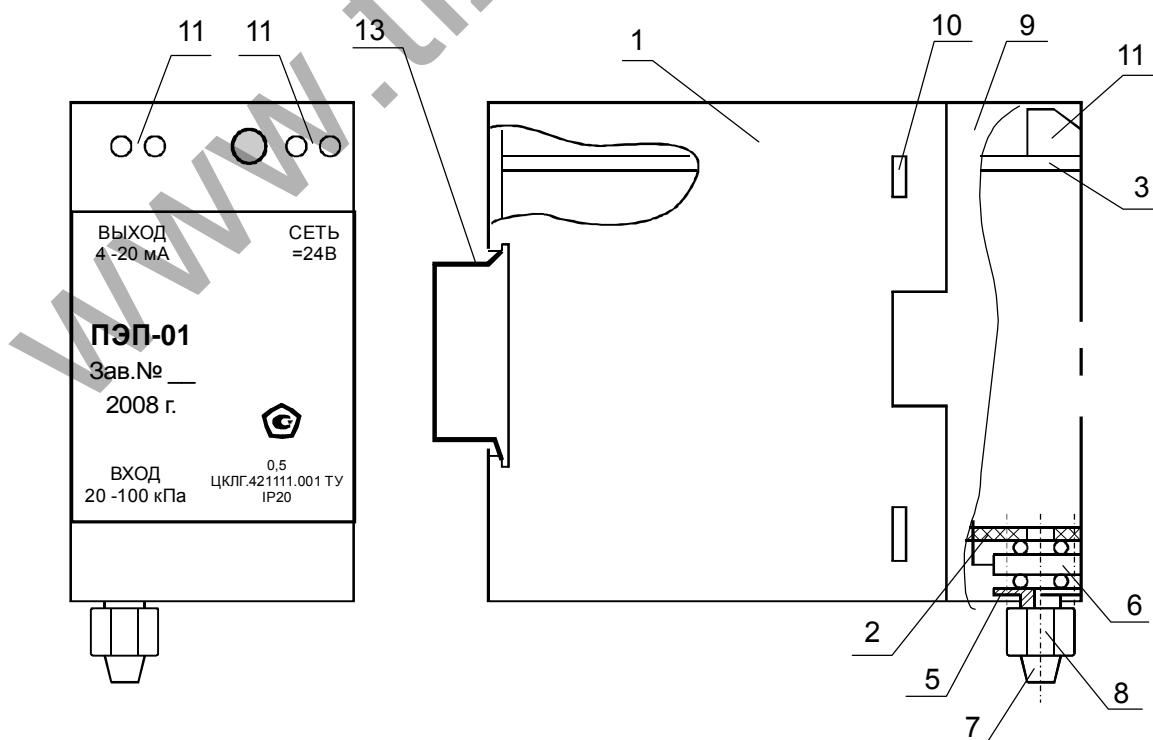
Внешний вид и конструкция ПЭП
